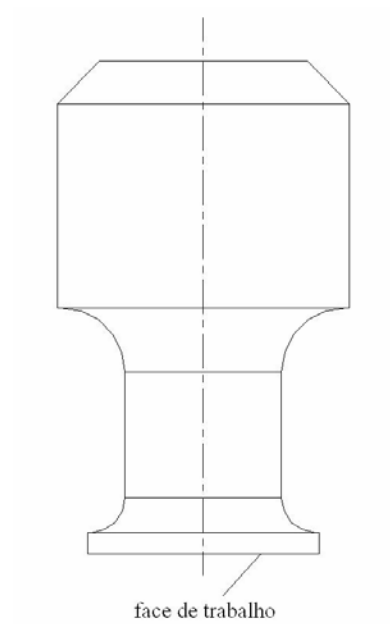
Sonotrodo cilíndrico usado no processo de corte e soldagem de tecidos sintéticos por ultra-som.
